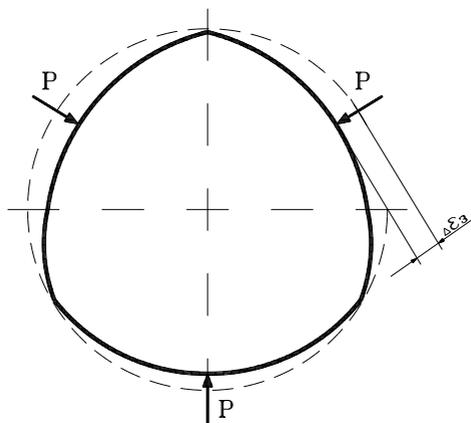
Погрешность закрепления цилиндрической заготовки в трехкулачковом патроне
